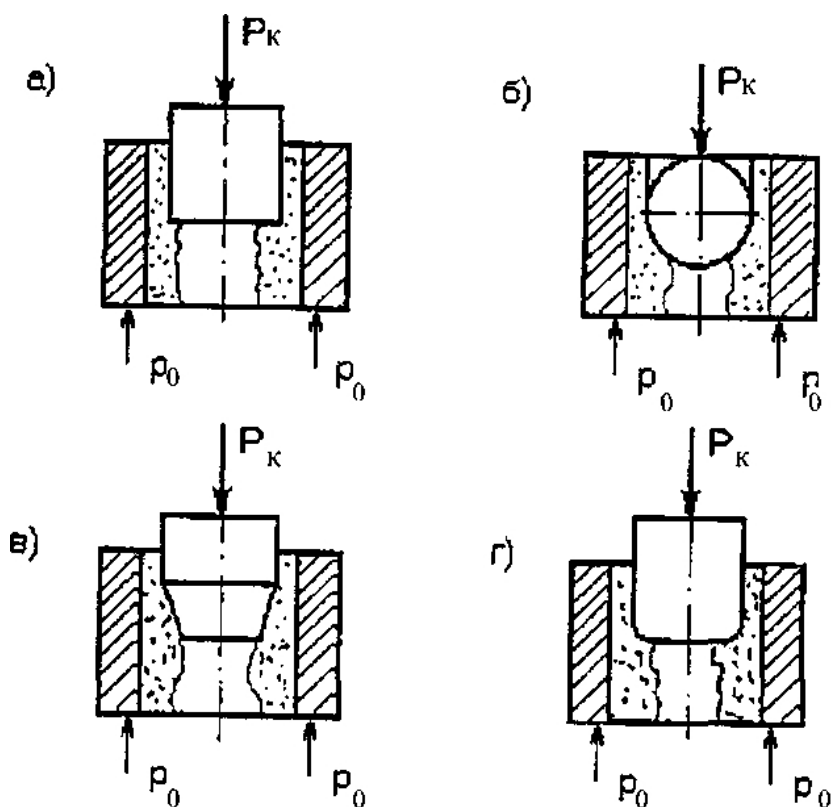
Схема динамічного формування шару композиції шляхом використання калібрів (P_k – сила калібрування. P_0 – опорна реакція): а) циліндричним калібром; б) сферичним калібром; в) циліндричним калібром із конусною фаскою; г) циліндричним калібром зі сферичною фаскою.
